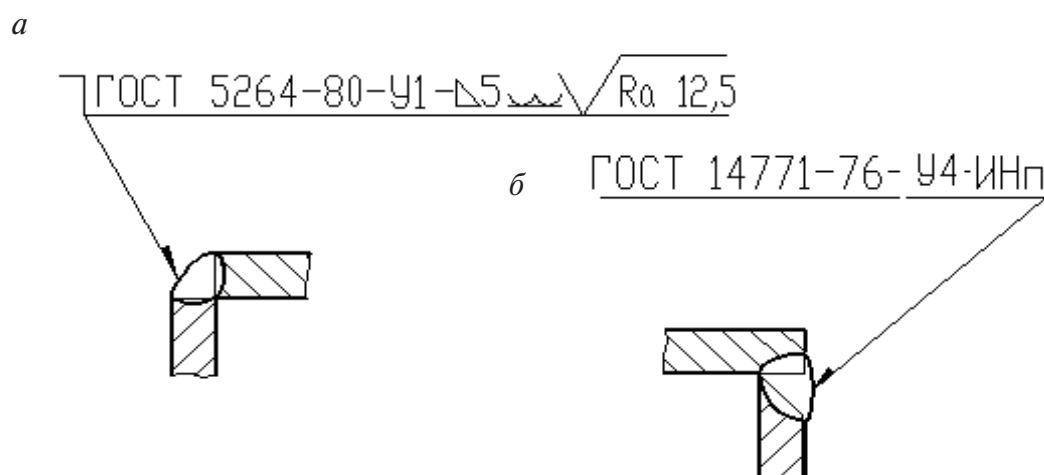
Примеры обозначения углового сварного шва:
